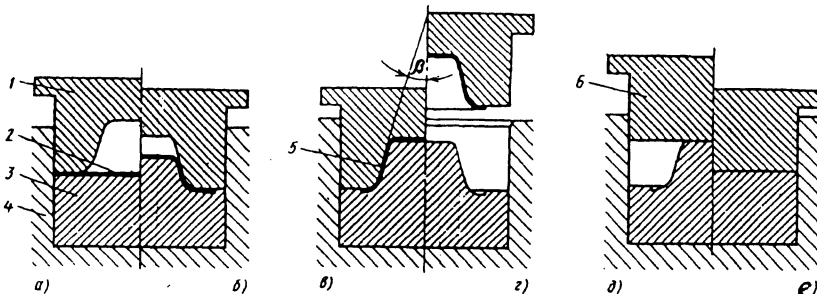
Схема штамповки-вытяжки пластичным металлом (свинцом)
